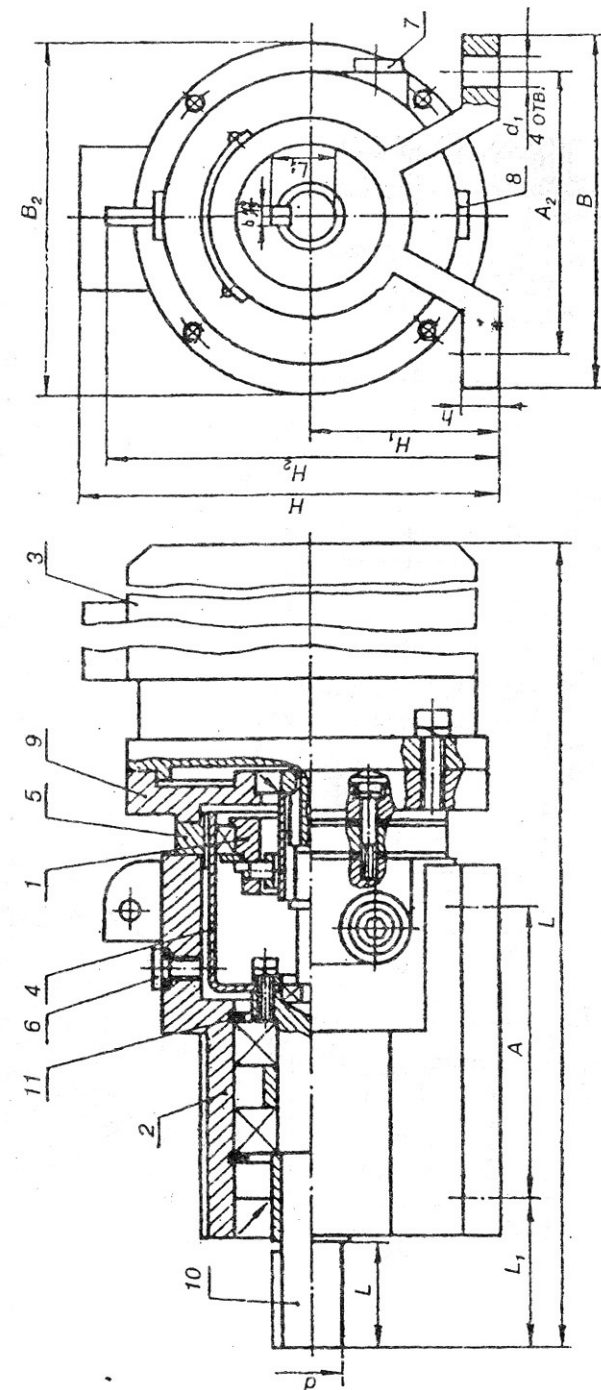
Мотор-редукторы волновые зубчатые типа 3МВ₃ в исполнении на лапах.
